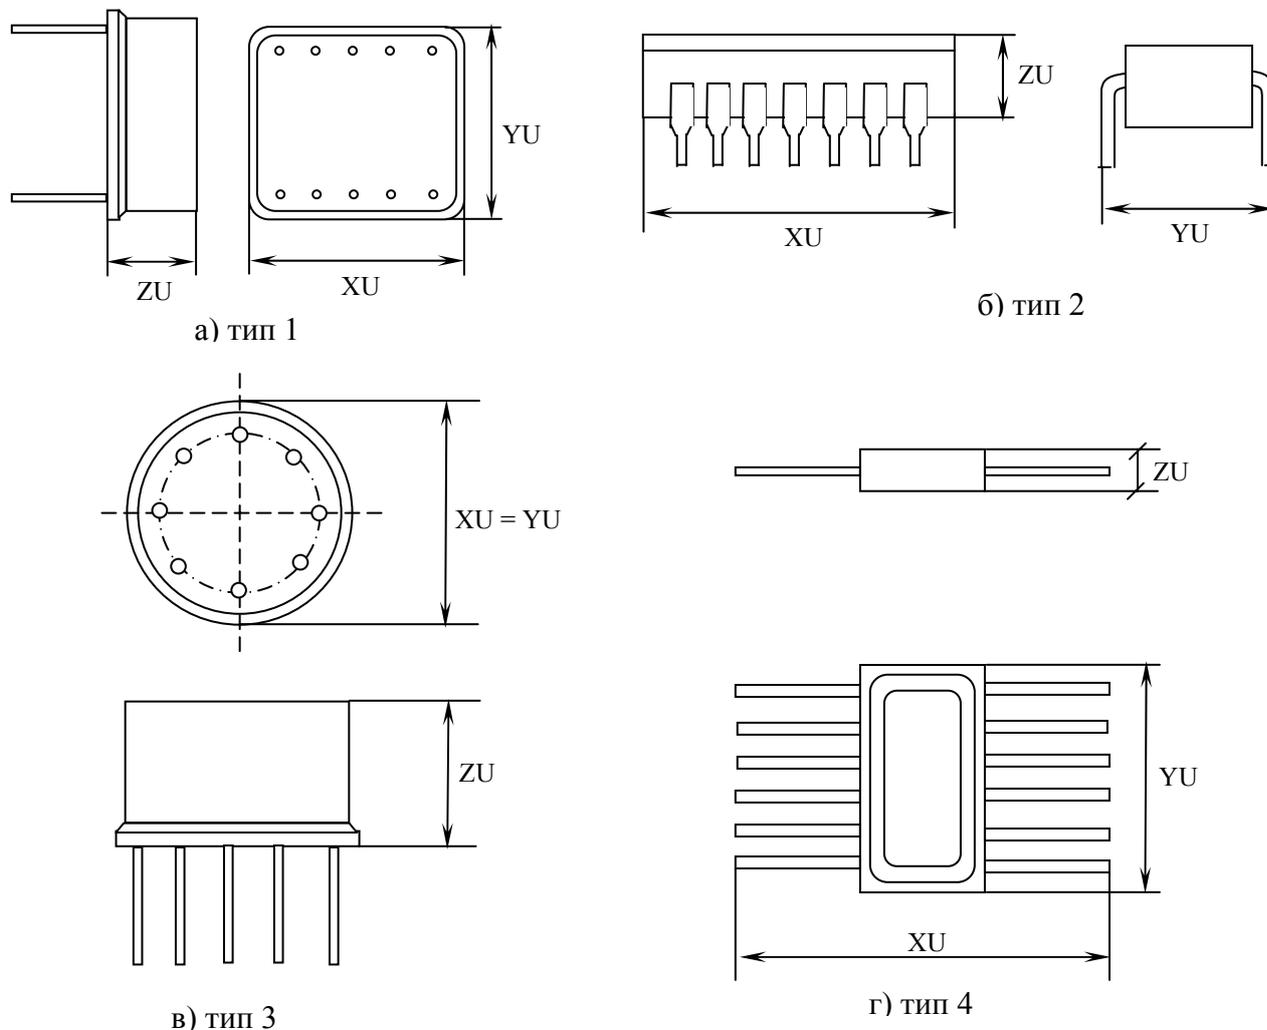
Установочные размеры корпусов: а – тип 1; б – тип 2; в – тип 3; г – тип 4
